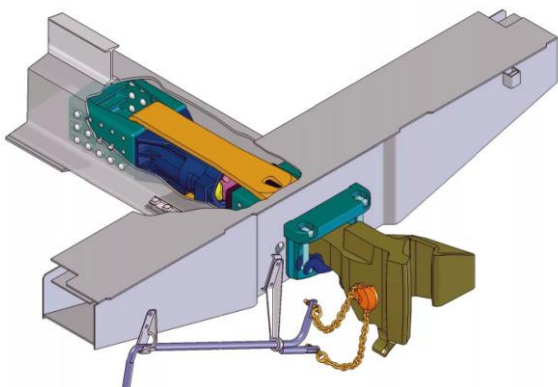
Общий вид автосцепного устройства с автосцепкой СА-3У полужесткого типа
